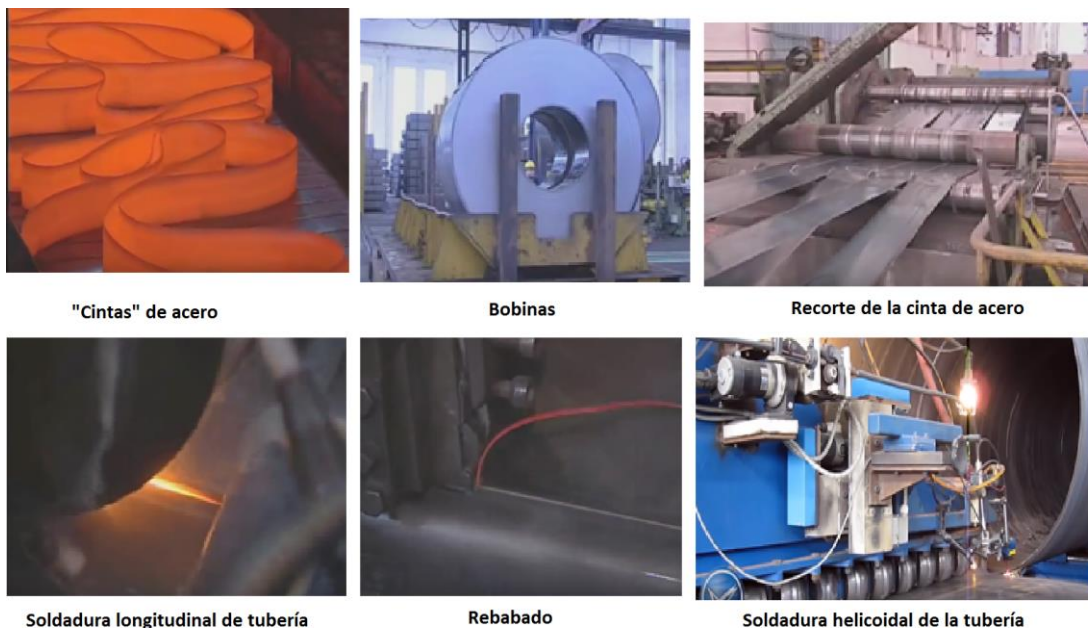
Proceso de revestimiento soldado (se ilustran dos tipos de soldadura) (AFTA, 2012).
